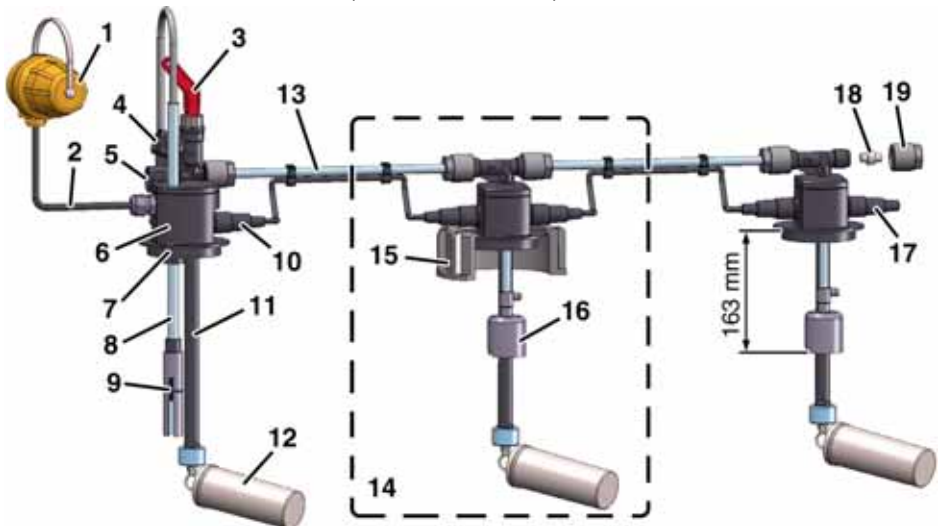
Grundeinheit mit GWG 12 K/1R-SWS und Erweiterung mit Schwimmerschalter
